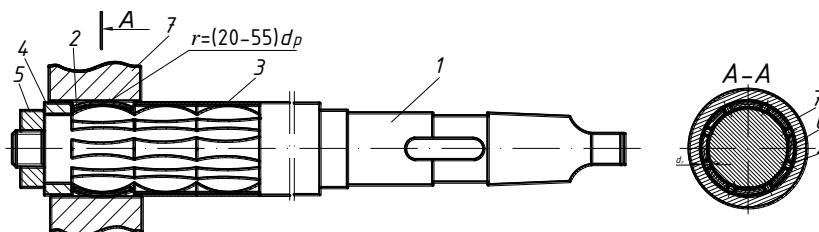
Пристрій для розкатування нежорстких втулок гнучкими роликами
